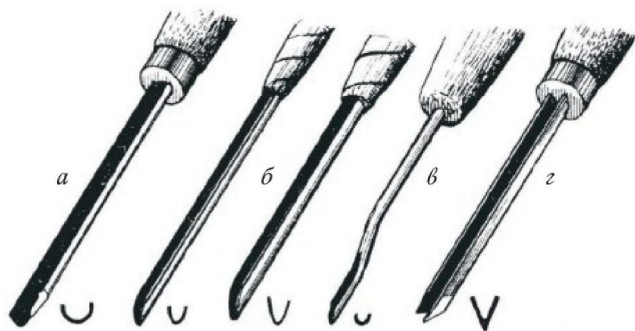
Царазики и уголок: а) стандартный царазик; б) царазик из растяжек зонтика; в) царазик, выполненный сверлением отверстия в стержне; г) изготовленный из круглого стержня сверлением канала с торца
